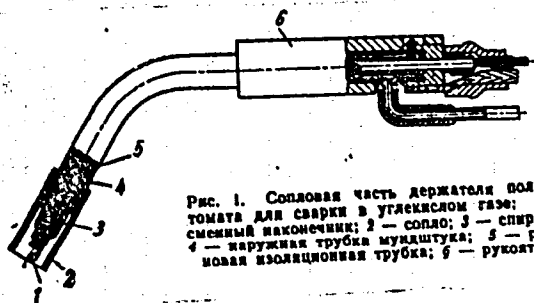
Сопловая часть держателя полуавтомата для сварки в углекислом газе: 1 — сменный наконечник; 2 — сопло; 3 — спираль; 4 — наружная трубка муфштук; 5 — резиновая изоляционная трубка; 6 — рукоятка.
